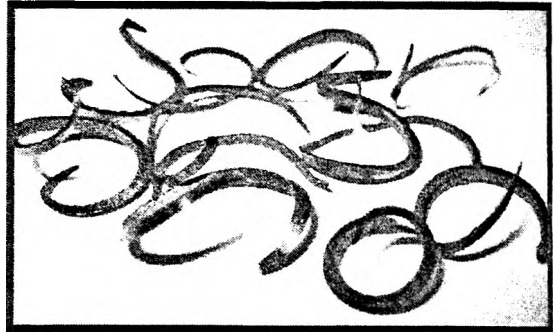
Виды стружек при обработке сталей фрезами MILL SHRED
